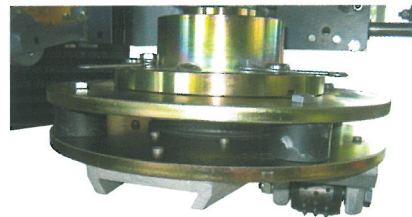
Elastisch gelagerte Grundplatte mit Schwalbenschwanzaufnahmen, eine Aufnahme mit Stokwalze besetzt
